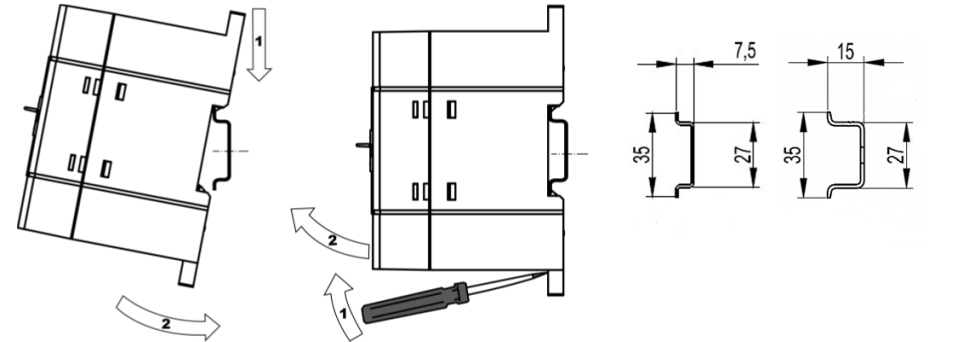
Монтаж прибора с креплением на DIN-рейку
